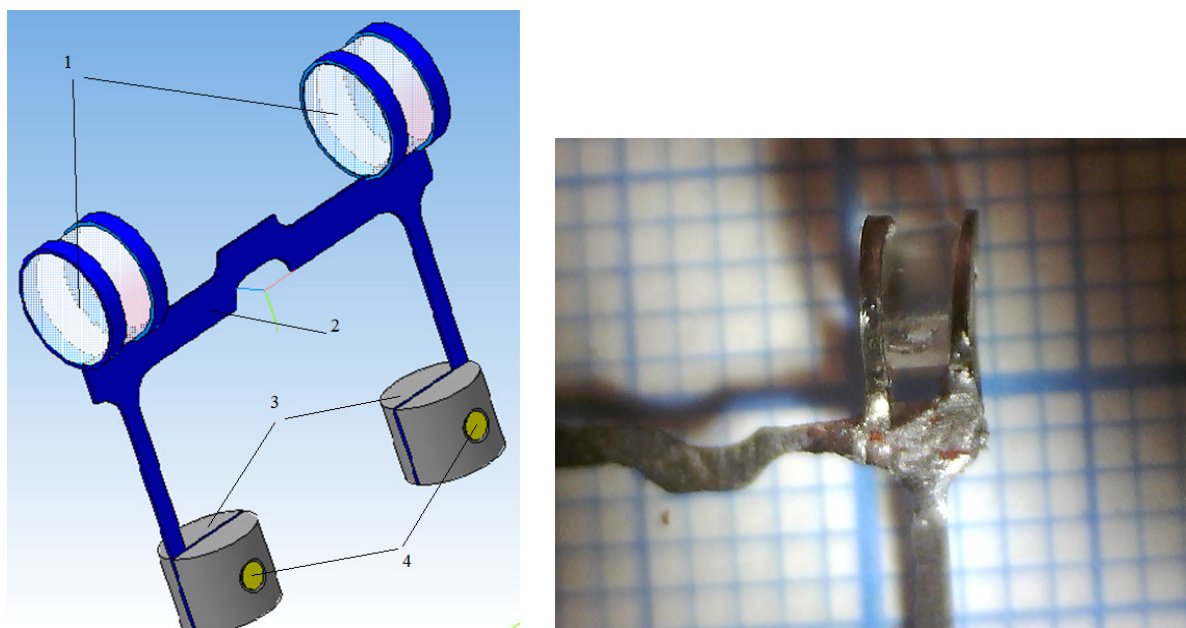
3D-модель и макетный образец чувствительного элемента:
